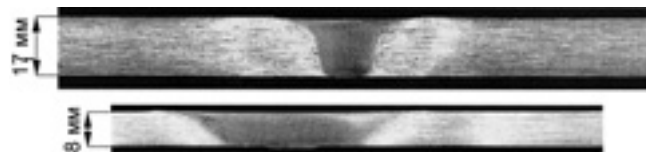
Макроструктура сварных соединений прессованных полос из сплава системы Al—Zn—Mg—Cu, выполненных СТП
